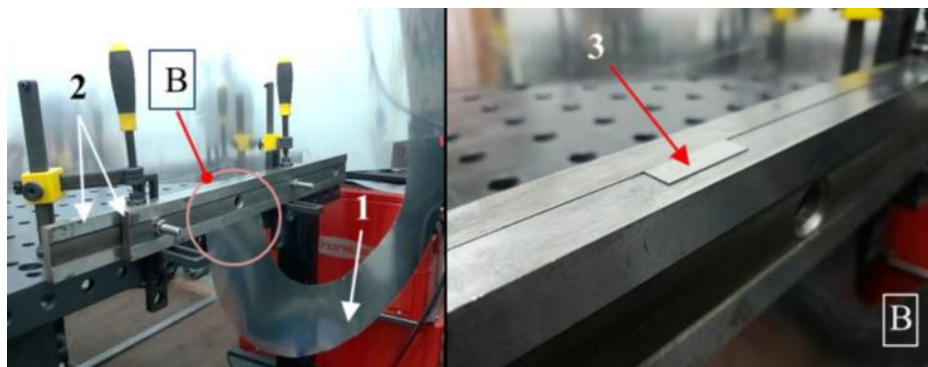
Пристрій для відборткування кромки заготовок під зварювання
